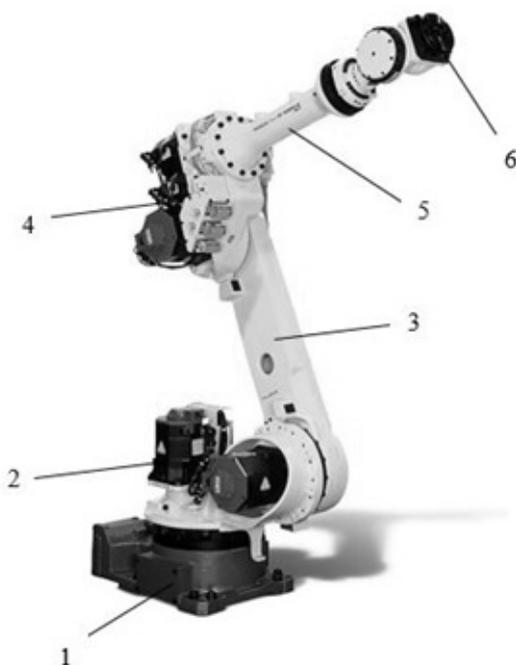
Робот манипулятор японской фирмы FANUC R-1000iA/80F: 1-основание; 2-привод робота; 3-корпус; 4-привод руки; 5-рука робота; 6-крепление для рабочего органа (хвата). [4]
